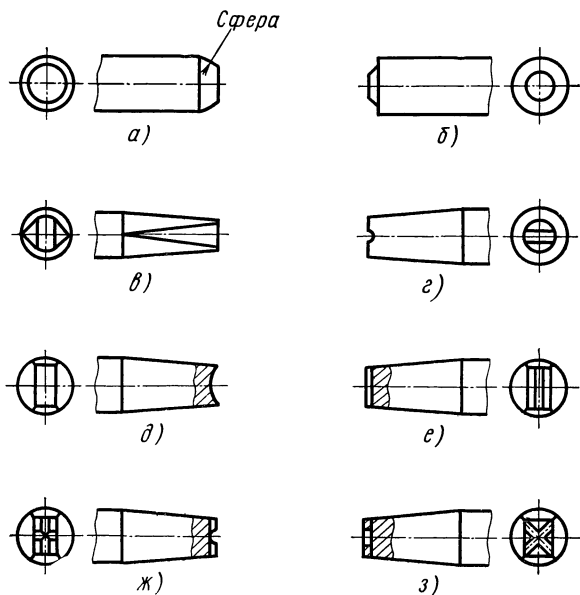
Форма рабочей части ультразвуковых сварочных инструментов
